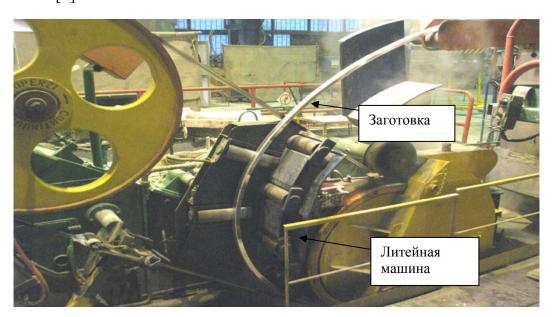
Общий вид машины непрерывного литья алюминия
